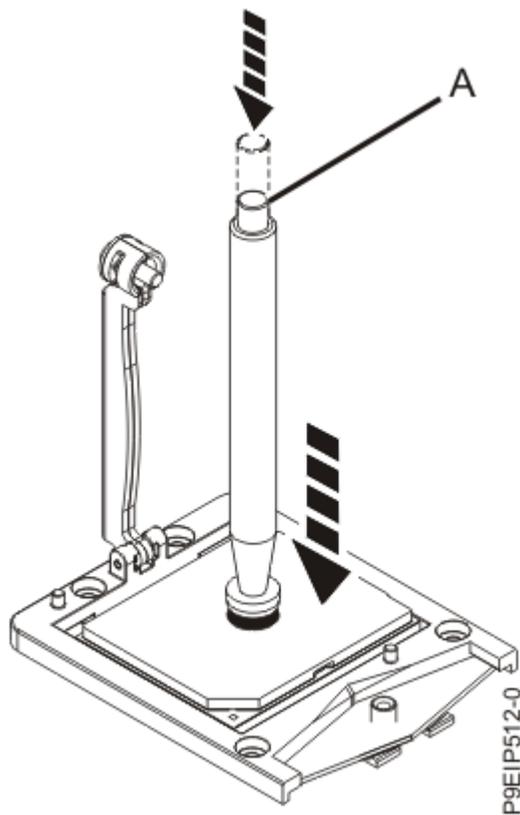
Ausbauwerkzeug auf das Systemprozessormodul herabsenken
